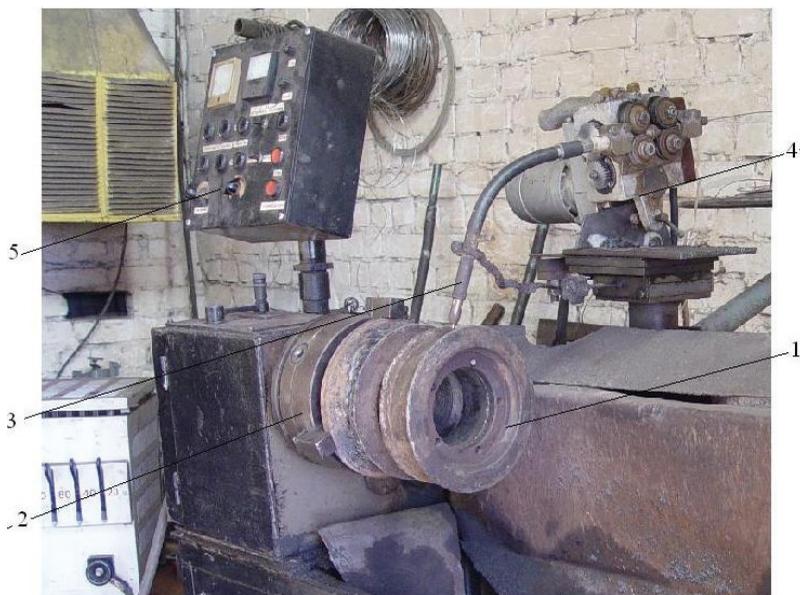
Наплавка опорного катка гусеничного трактора порошковой проволокой на установке УД-209: 1 – каток; 2 – зажимной патрон; 3 – горелка; 4 – подающий механизм; 5 – пульт управления
